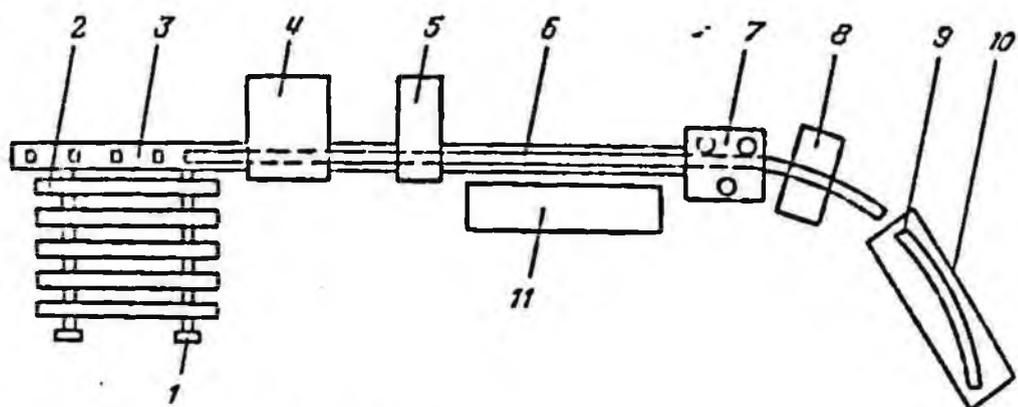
Схема безотходной технологической линии изготовления крепей: 1 — стеллаж; 2 — пруток спецпрофиля; 3 — рольганг; 4 — сварочная машина; 5 — пресс для рубки прямолинейных элементов крепей; 6 — сваренные прутки спецпрофиля; 7 — гибочная машина; 8 — машина для резки элементов; 9 — готовый элемент крепей; 10, 11 — пакетирующая машина соответственно для криволинейных и прямолинейных элементов
